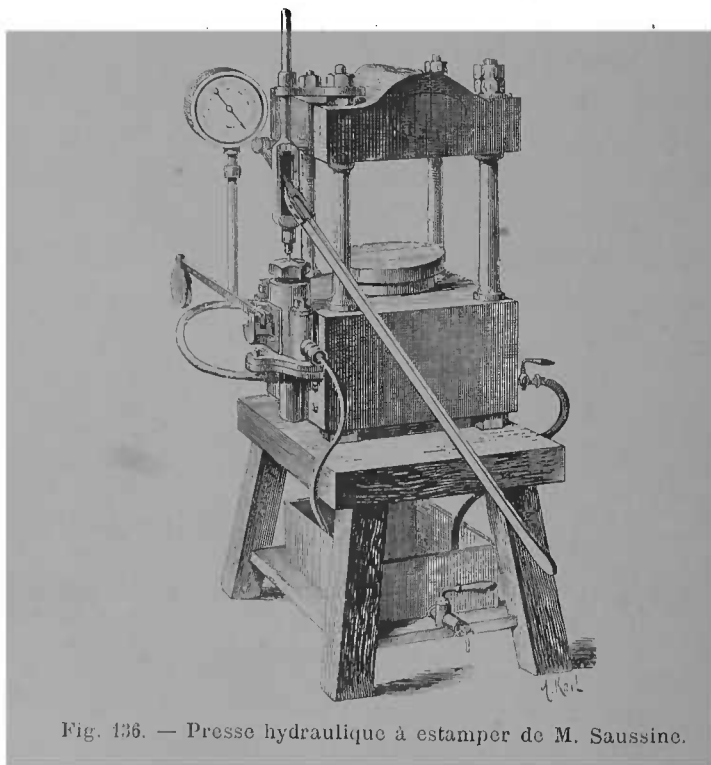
Presse hydraulique à estamper de M. Saussine.
